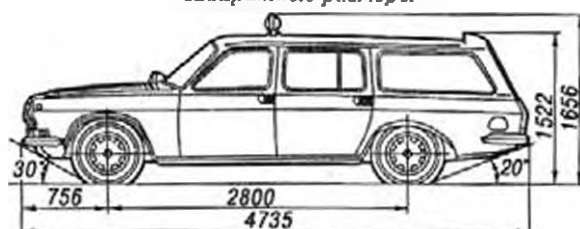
Автомобиль ГАЗ-24-13 "Волга" и его габаритные размеры
